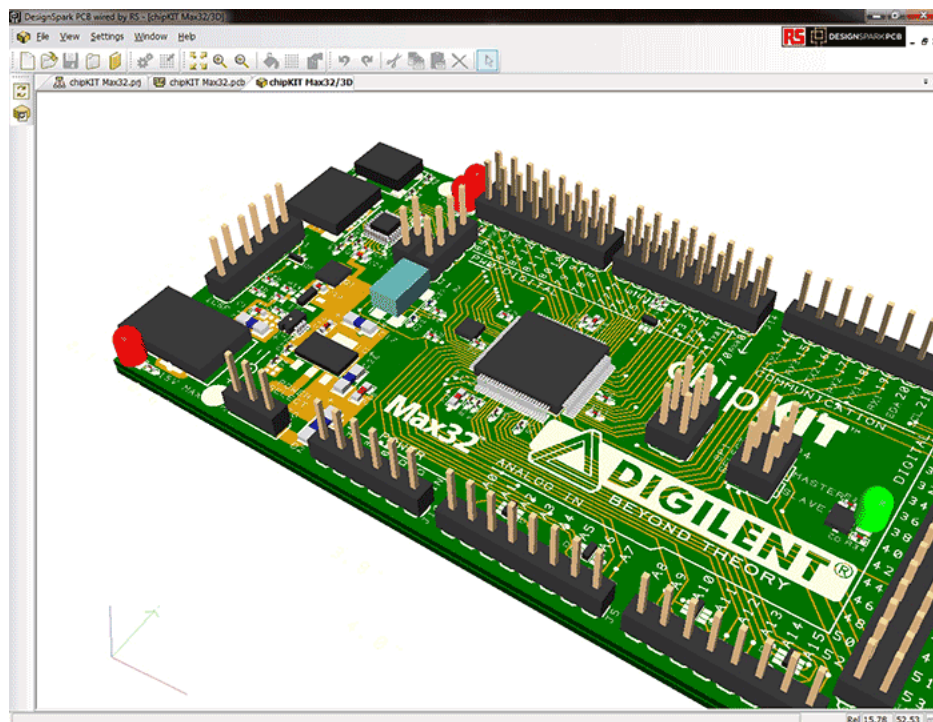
Трехмерная модель печатной платы в САПР DesignSpark PCB
